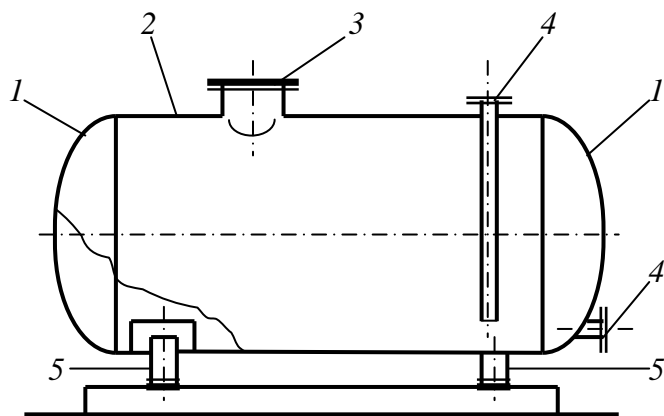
Сварная горизонтальная цилиндрическая емкость с эллиптическими днищами: 1—днища (крышки); 2—корпус; 3—смотровой люк (лаз); 4—патрубки (штуцеры); 5—опоры (лапы)
